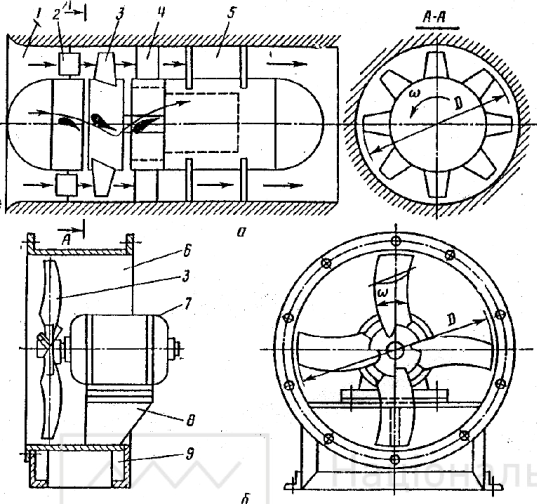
Схеми осьових вентиляторів: а) з напрямним апаратом; б) без напрямного апарату (тип МЦ); 1- горловина; 2- напрямний апарат; 3- робоче колесо; 4- випрямний апарат; 5- дифузор; 6- корпус; 7- електродвигун; 8- кронштейн; 9- опорна стійка
